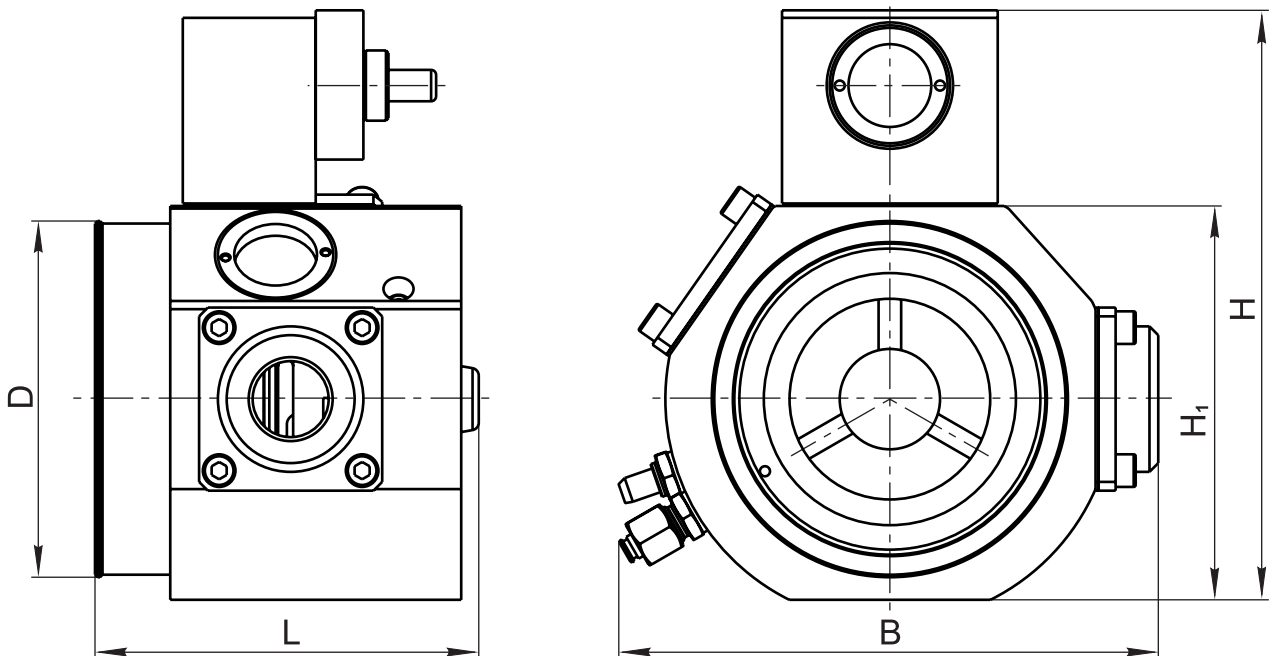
Габаритные и присоединительные размеры для смесителей типа СГ...-Р
